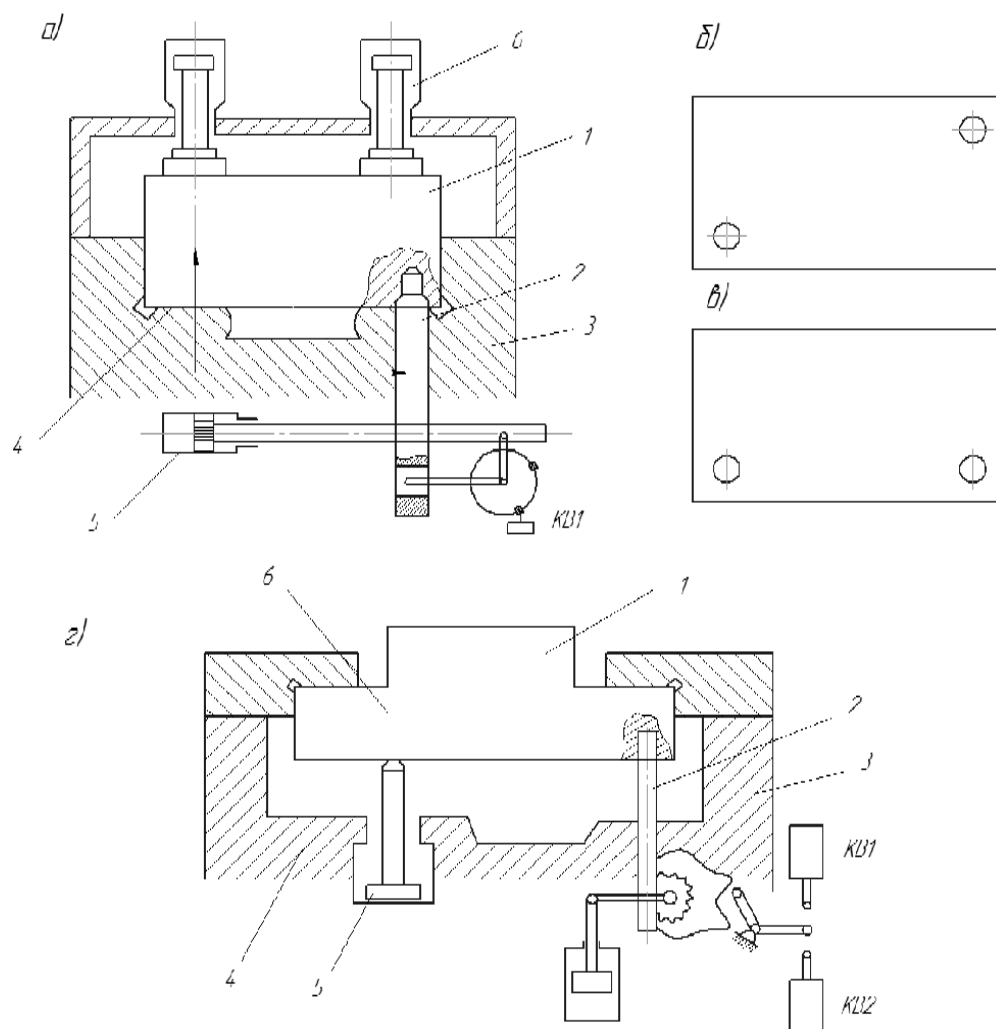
Схема затискування і фіксації заготовок
